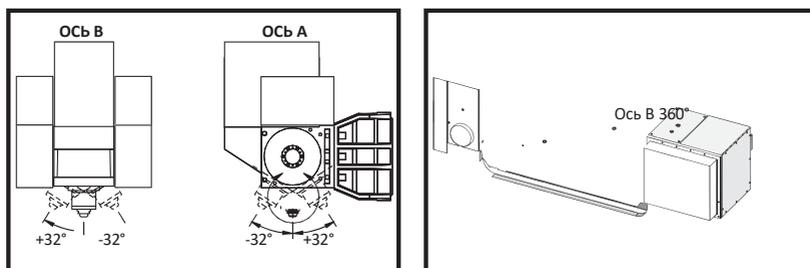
Движение осей на фрезерном станке VR-11 и HAAS TRT 210
